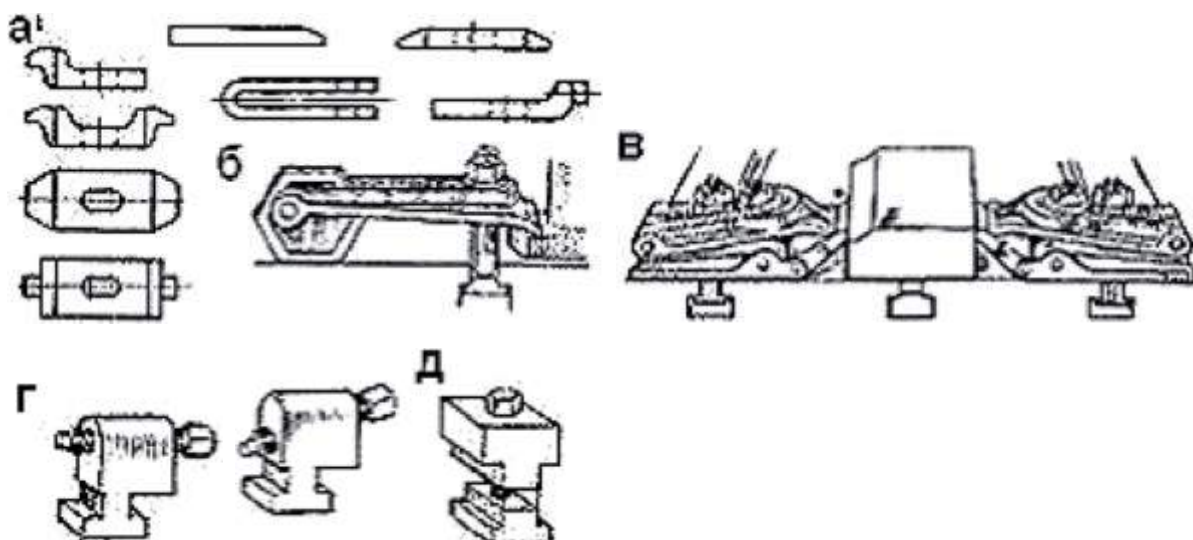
Приспособления для закрепления на столе станка: а - прихваты; б — универсальный прихват с подставкой; в - пример закрепления заготовки прихватами; г - винтовые прижимы; д - упор
